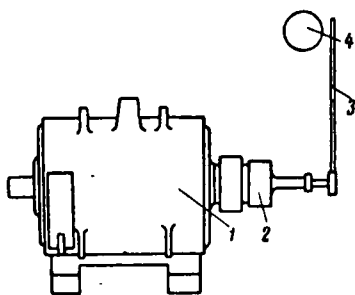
Место рабочего при снятии шестерни с вала тягового двигателя:
